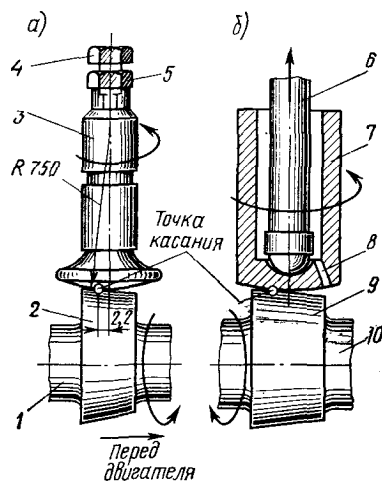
Тарельчатый (а) и цилиндрический (б) толкатели
